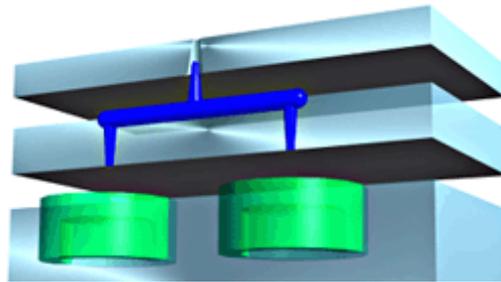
Molde de tres placas. Fuente: Autodesk [23]
